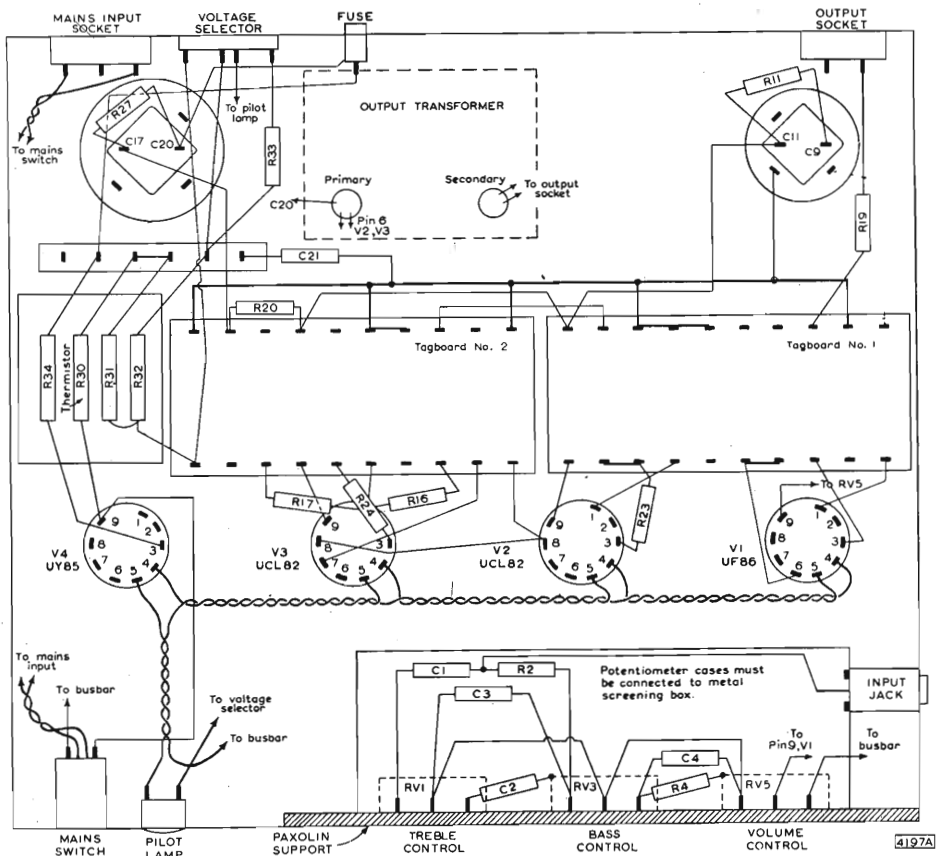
Il cablaggio dell'amplificatore da 7 W visto dal lato componenti.
